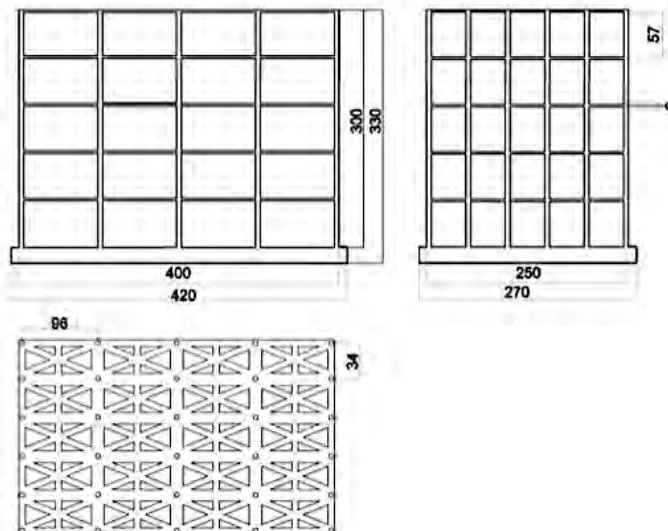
Чертеж решетчатой конструкции: фронтальный вид, вид сверху, вид сбоку
